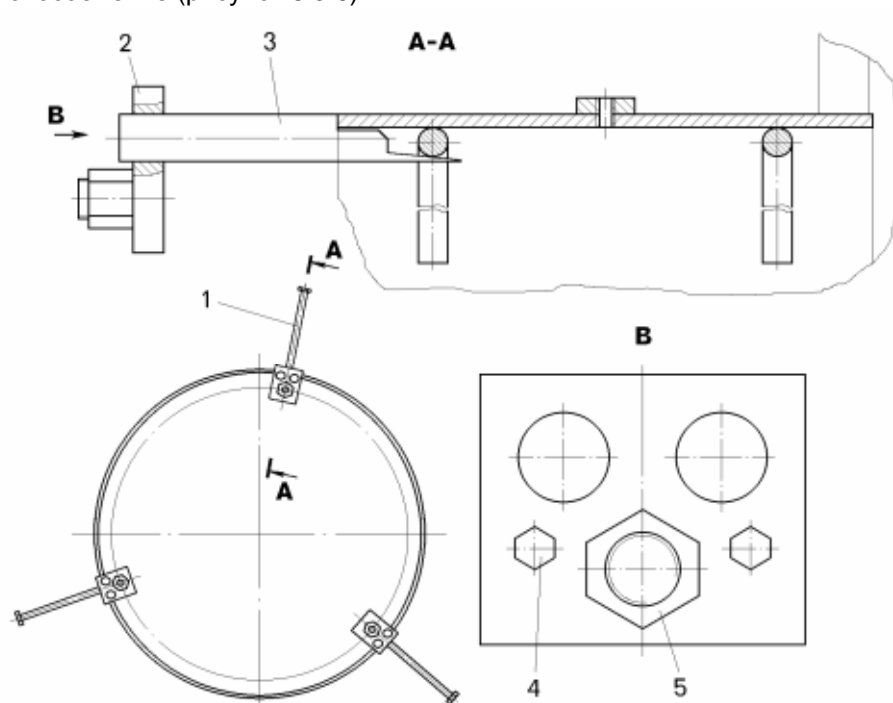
Приспособление для центровки внутреннего колеса с шиной на ступице при установке задних двоярных колес:
